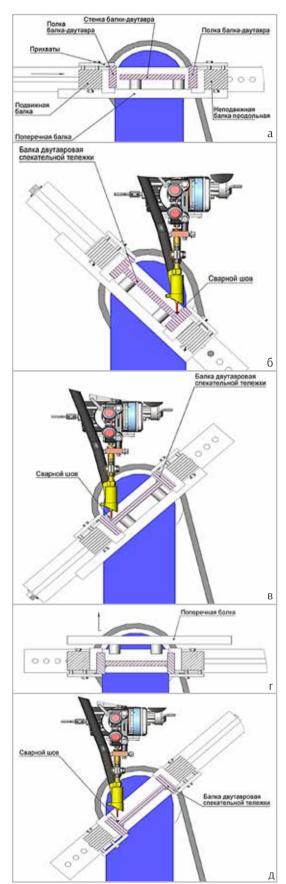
Последовательность сборки и сварки двутавровых балок на специализированной установке: а, Γ — сборка; б, в, д — сварка
